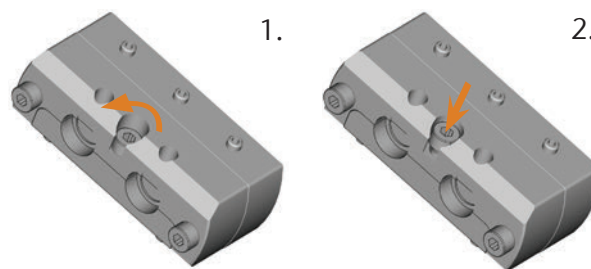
APERTURA DEL SOPORTE DE PILARES PREFACE®
